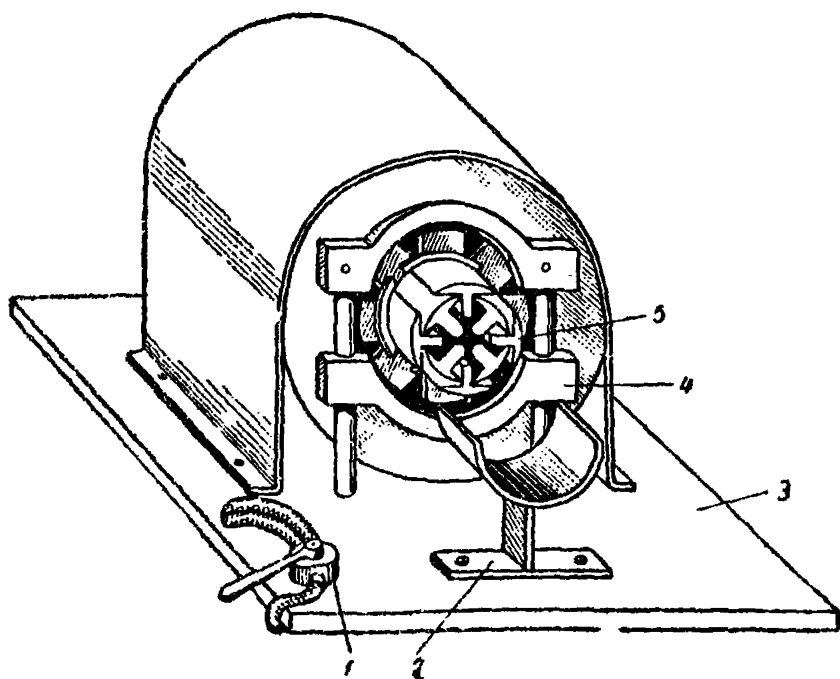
Станок с лепестковой головкой для изготовления раструбов
